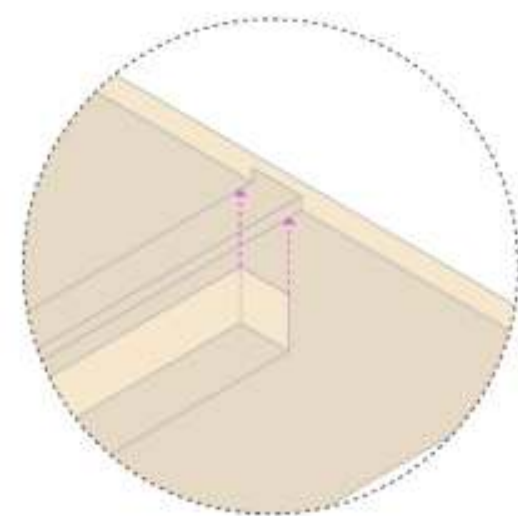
\_Diagrama de detalhe do encaixe dado joint entre a viga e a prateleira.
